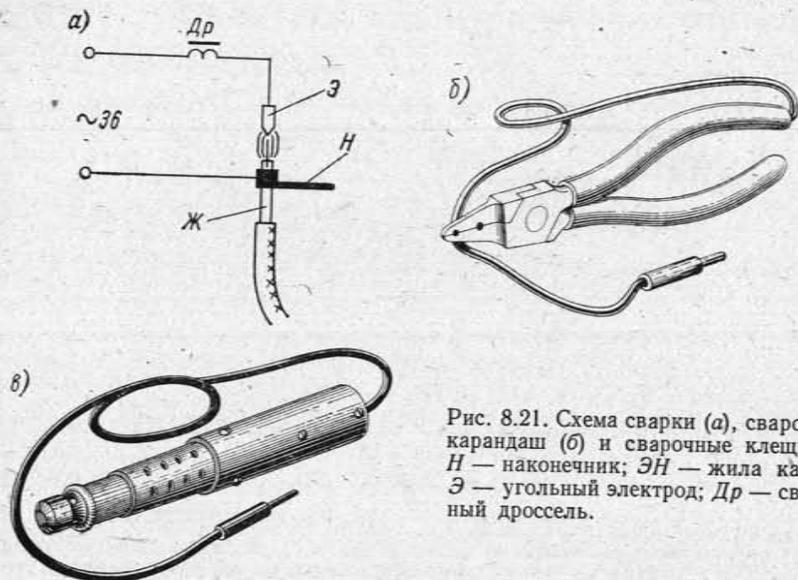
Схема сварки (а), сварочный карандаш (б) и сварочные клещи (в). Н — наконечник; ЭН — жила кабеля; Э — угольный электрод; Др — сварочный дроссель.
